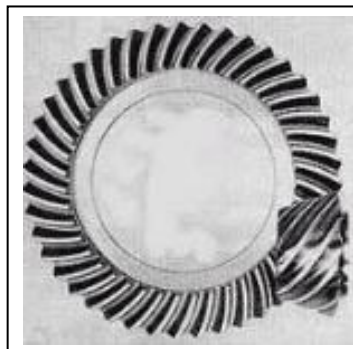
Engranajes Cónicos Hipoides⁷⁰
